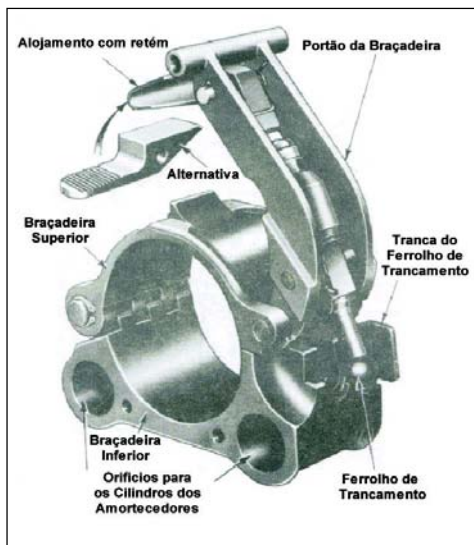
Braçadeira do Tubo do Bipé L5A4
